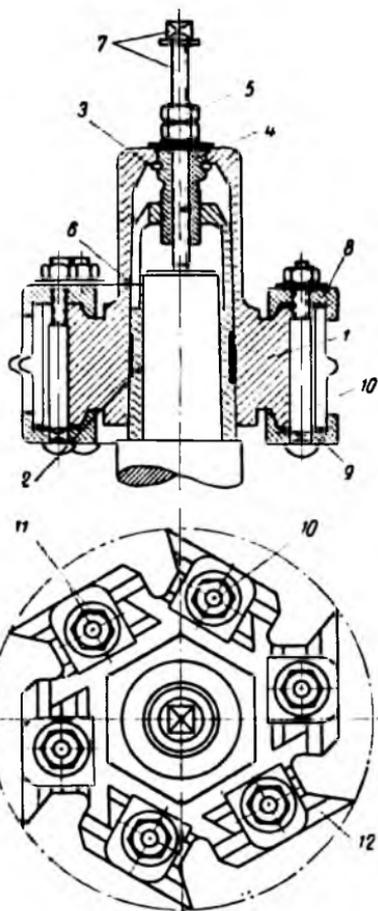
Многолезная фрезерная головка с прямыми резцами:
